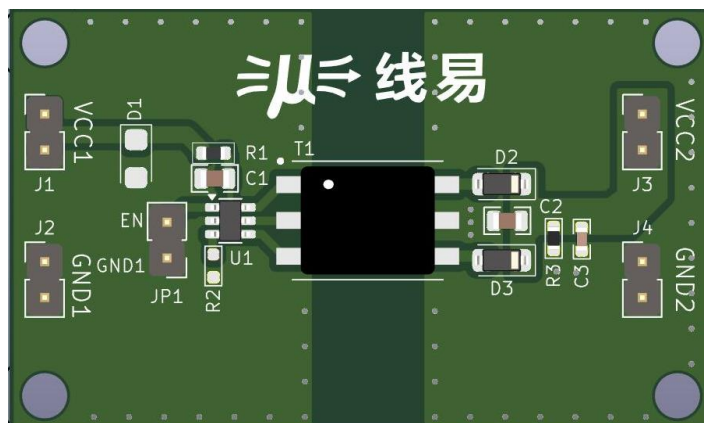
PCB 示意图(尺寸: 30x 50mm)
